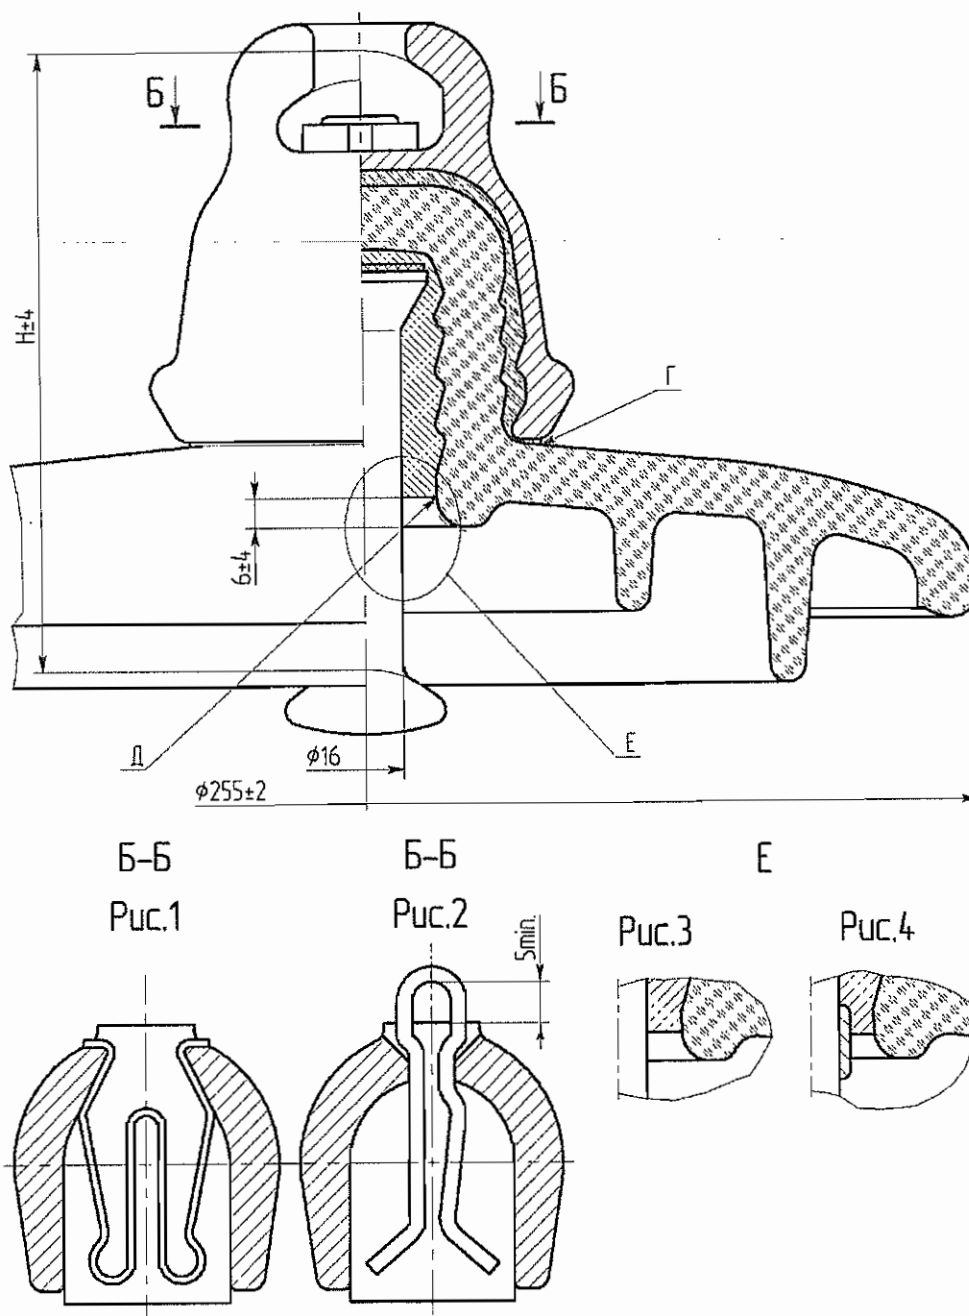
Габаритные, присоединительные и установочные размеры изолятора ПС 120Б
